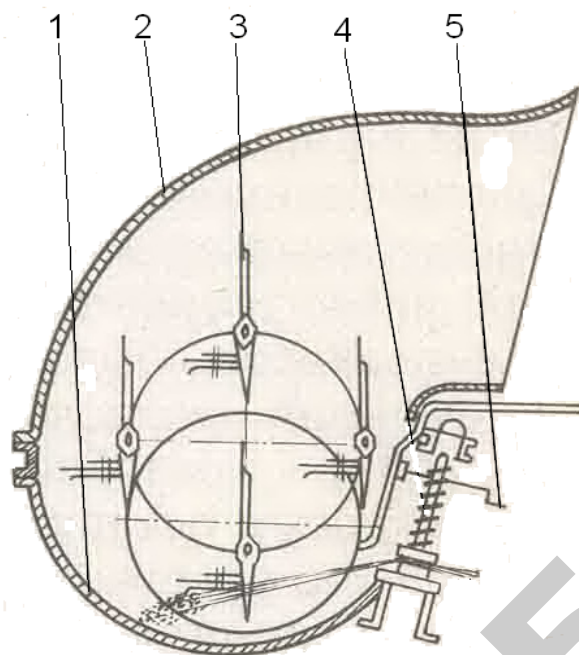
Камера очеса льноуборочного комбайна ЛК-4А:
